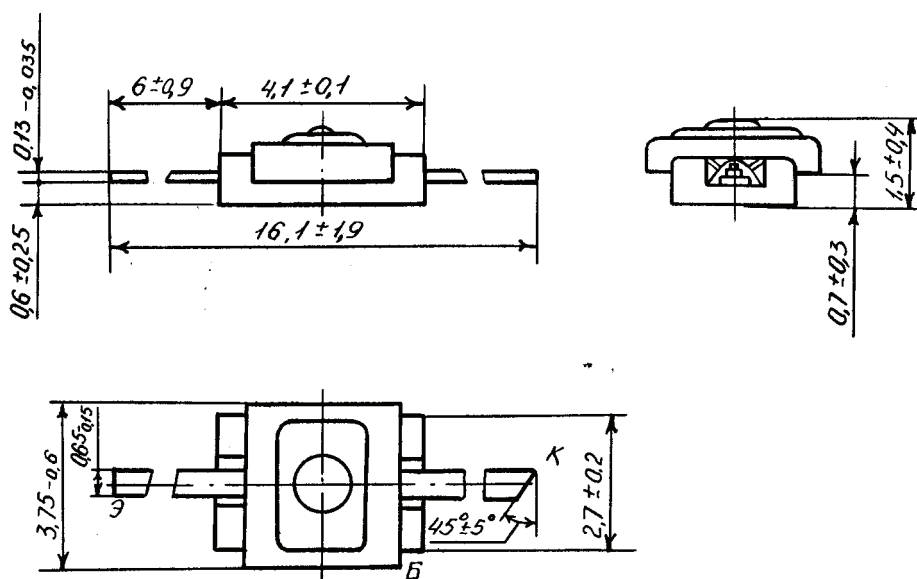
Габаритный чертеж КТ918А-2, КТ918Б-2
